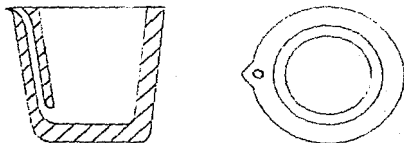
Corte seccional y vista en planta de una cuchara de colado en la cual el metal sale del fondo.
